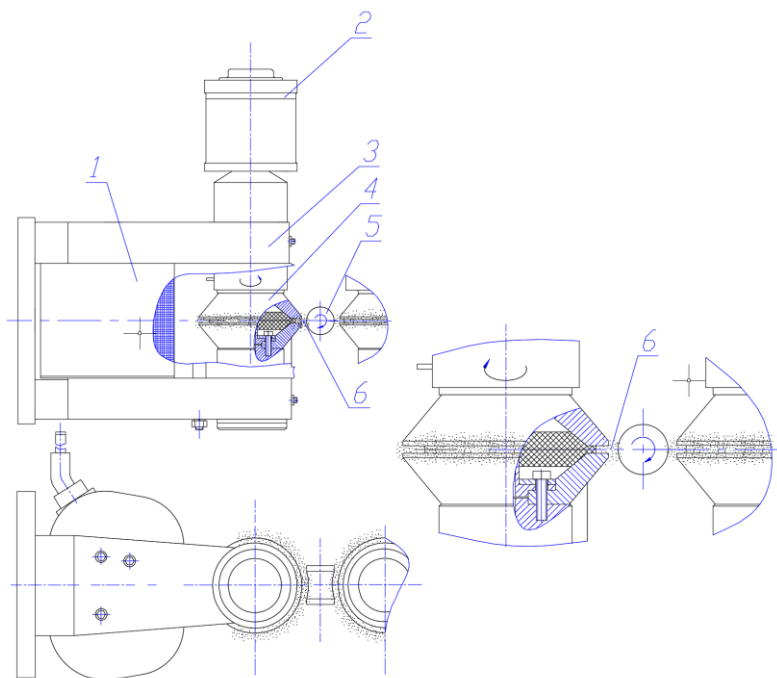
Схема исследовательской установки: индуктор (1); электродвигатель (2); магнитопровод (3); полюсный наконечник (4); обрабатываемая деталь (5); ферромагнитный порошок (6)
